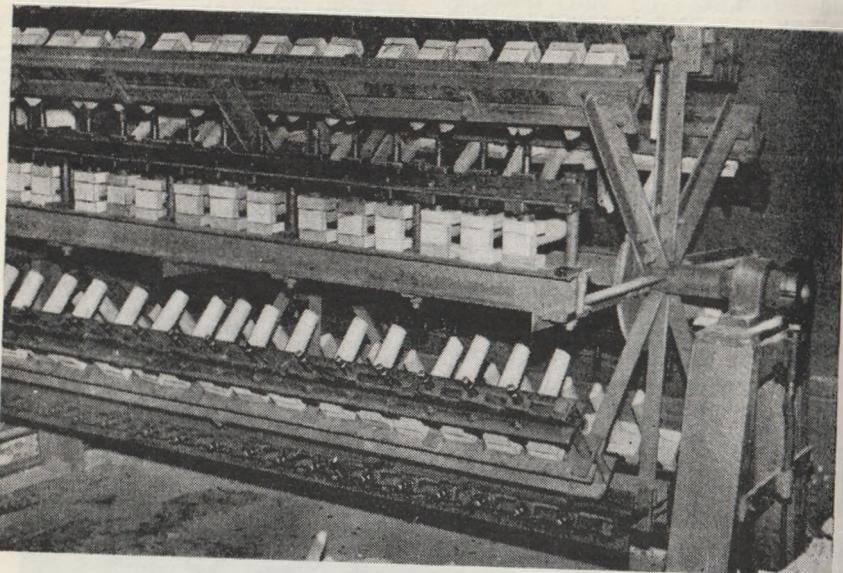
Клеильно-веерный пресс для приклевания наращений к ручкам мандолин
